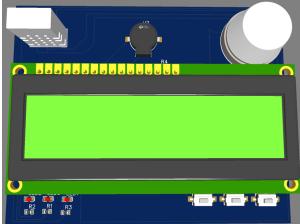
PCB do circuito 2 - PRODUTO UNICO 3D
